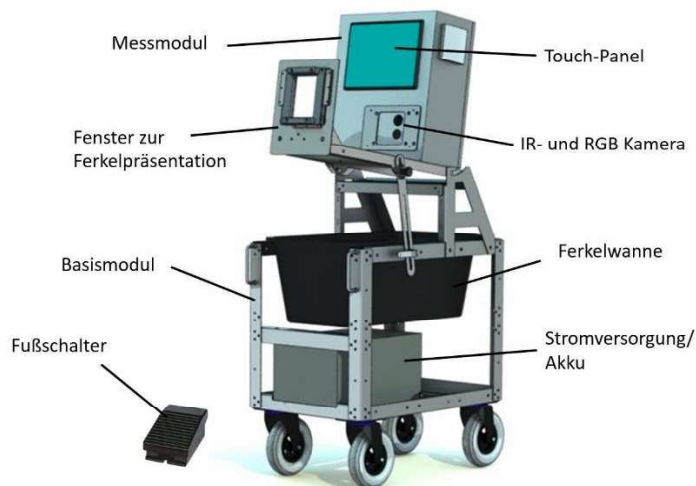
CAD-Baugruppe, Hauptkomponenten SINS-Messmodul
